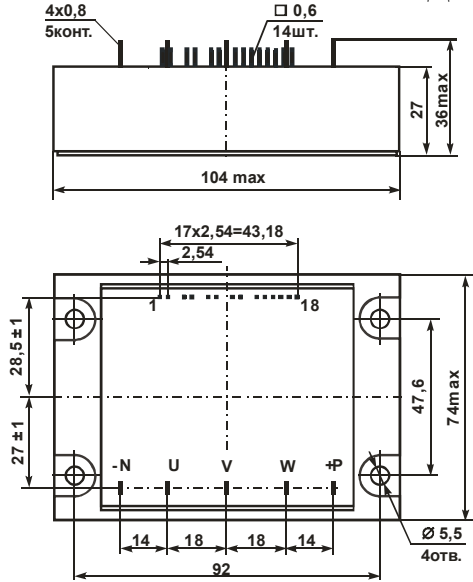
Габаритный чертеж модулей M13A-10-6(12)
